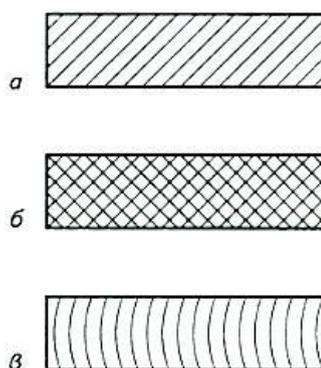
Виды штриховки деталей в сечениях и разрезах: а — металлы и твердые сплавы; б — неметаллические материалы; в — древесина
